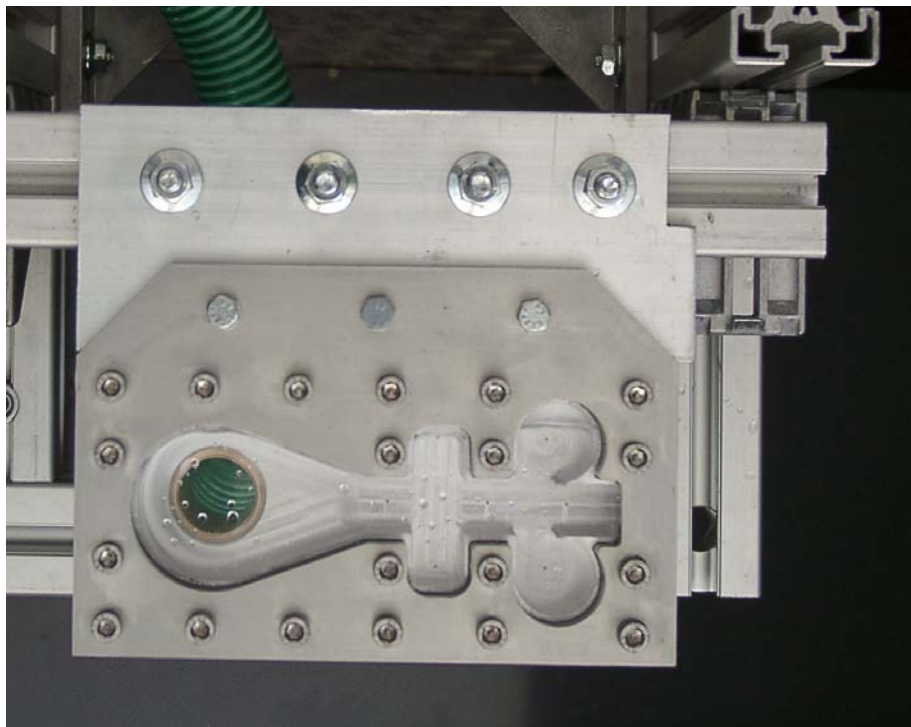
Eingebaute Düse mit Plexiglas-Deckel
